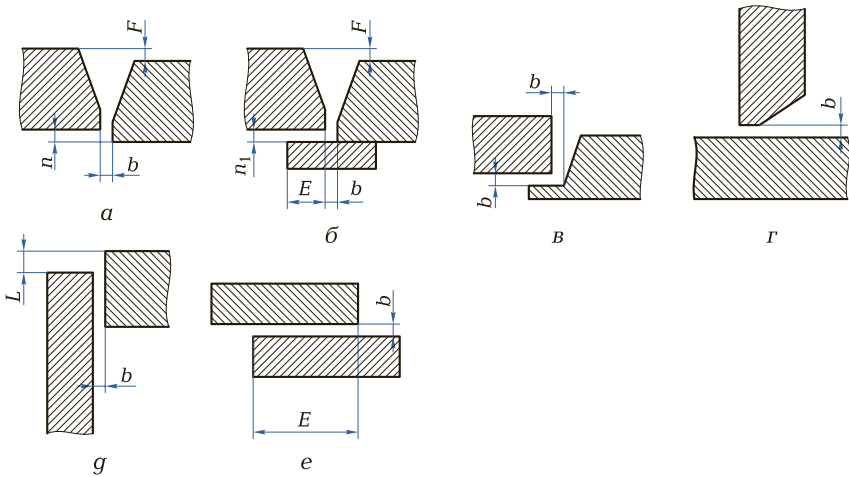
Размеры, контролируемые при сборке под сварку соединений разных типов:
